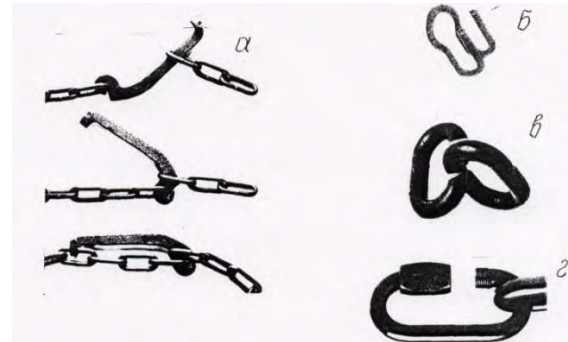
Соединительные элементы для установки цепей на колеса машин:
